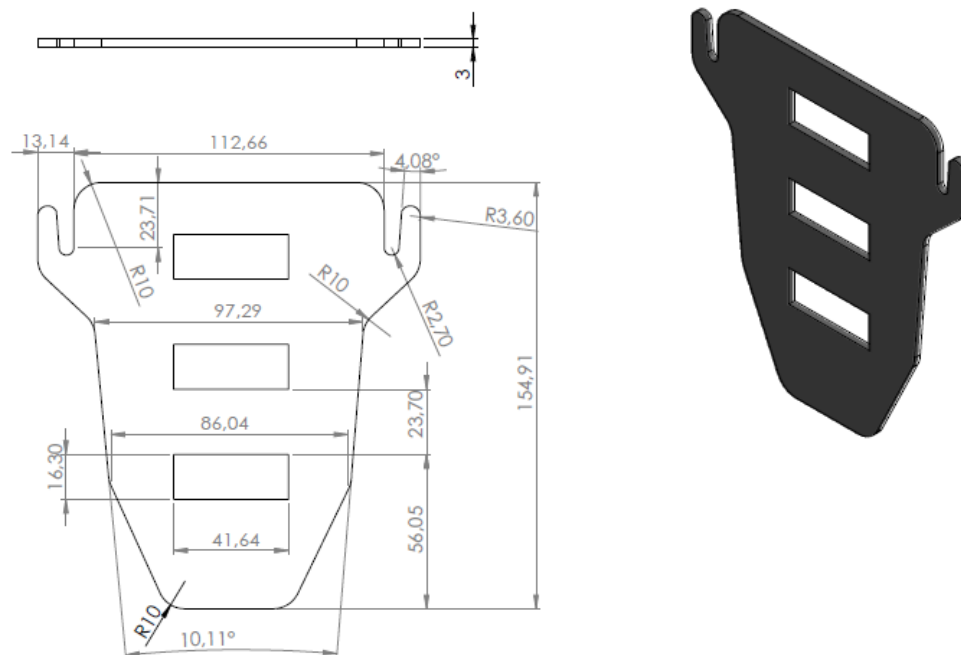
3D модель четвертой базы гексакоптера в SolidWorks
